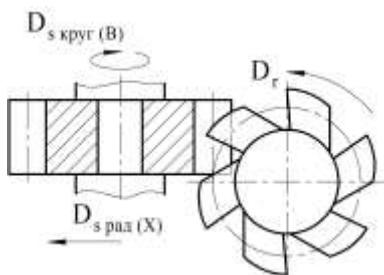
Формообразующие движения зубофрезерного станка при выходе из контакта
